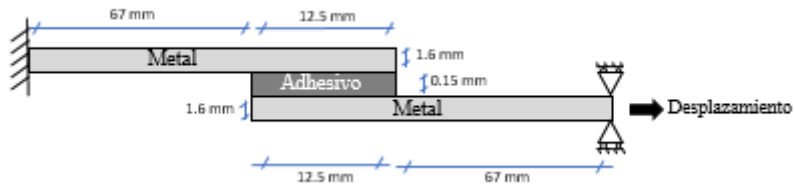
Dimensiones de unión a solape simple de la probeta real.
